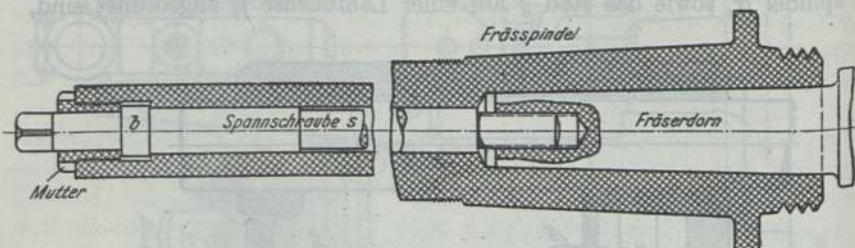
Einspannen des Fräasers mit einer Spannschraube.
